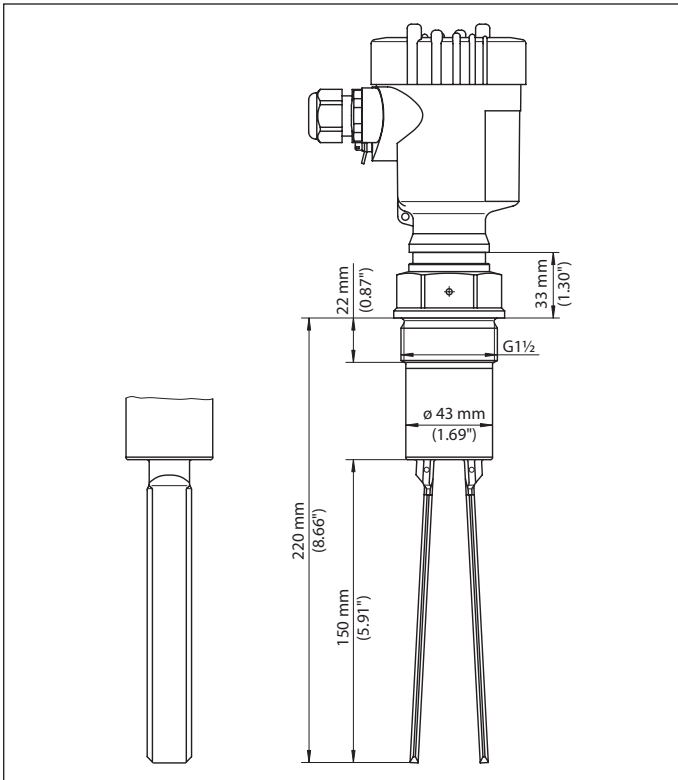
VEGAWAVE 61 - Gewindeausführung G1½
